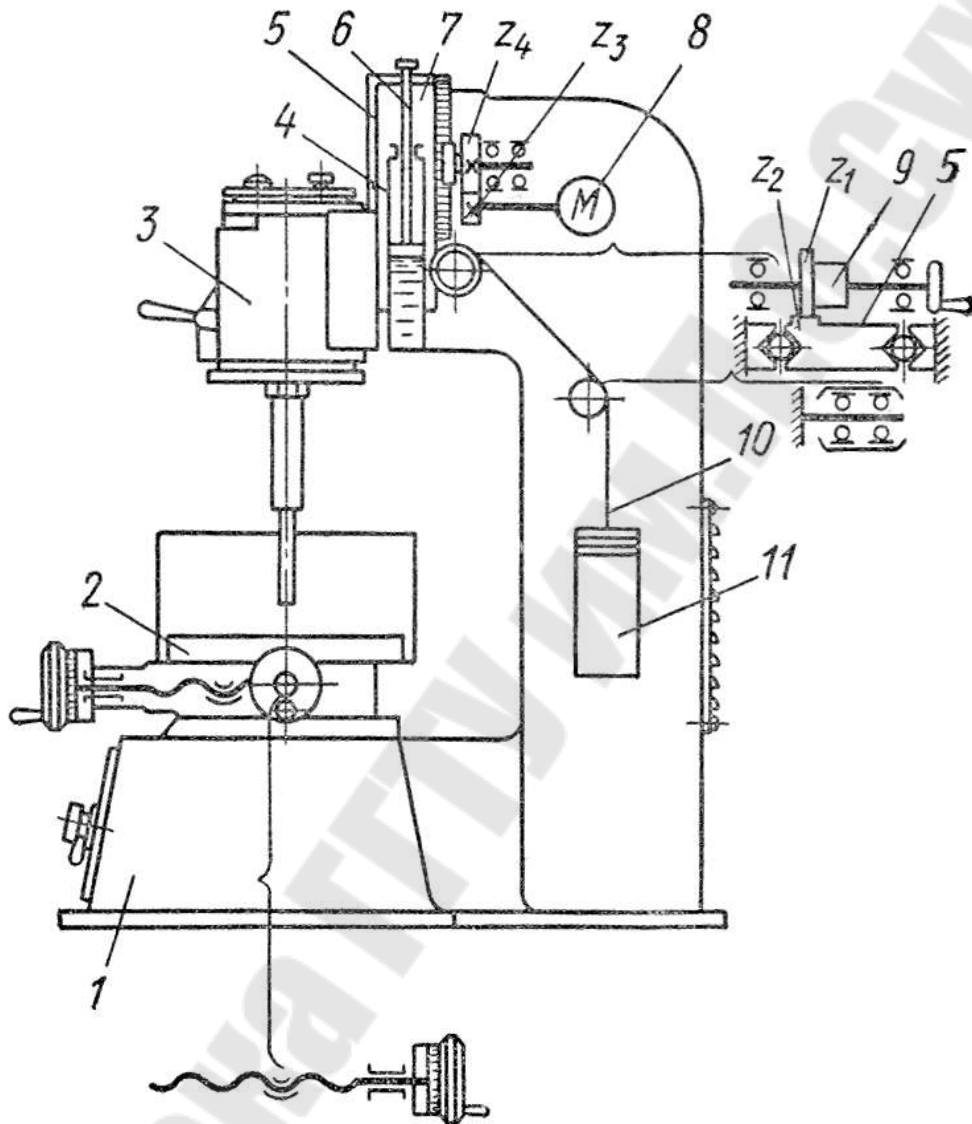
Кинематическая схема универсального прошивочного станка 4770
